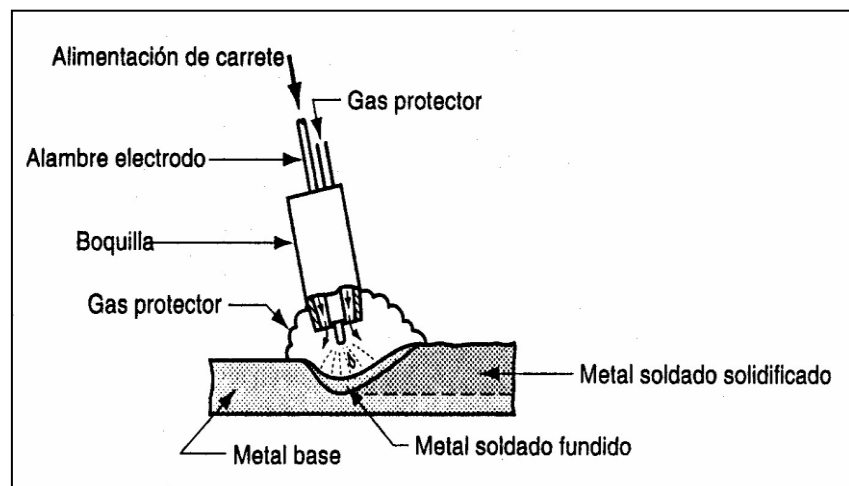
SOLDADURA METÁLICA CON ARCO ELÉCTRICO Y GAS (GMAW).
